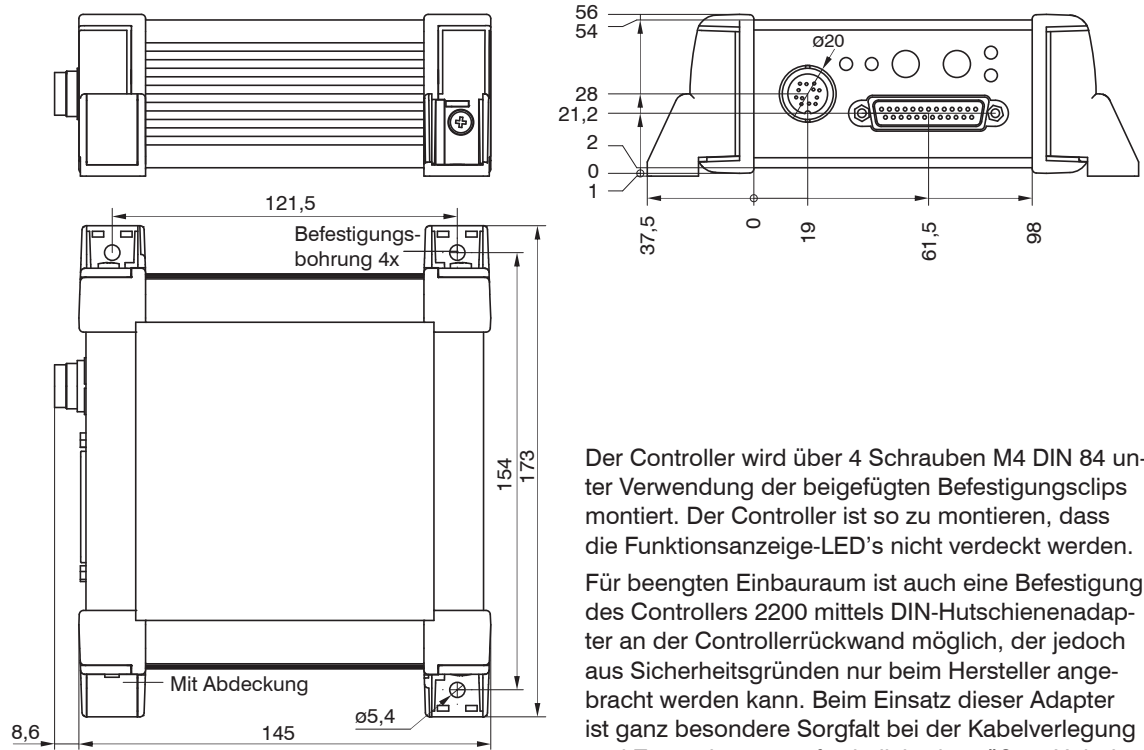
Maßzeichnung des Controllers mit Montagewinkel, Abmessungen in mm (nicht maßstabsgetreu)
